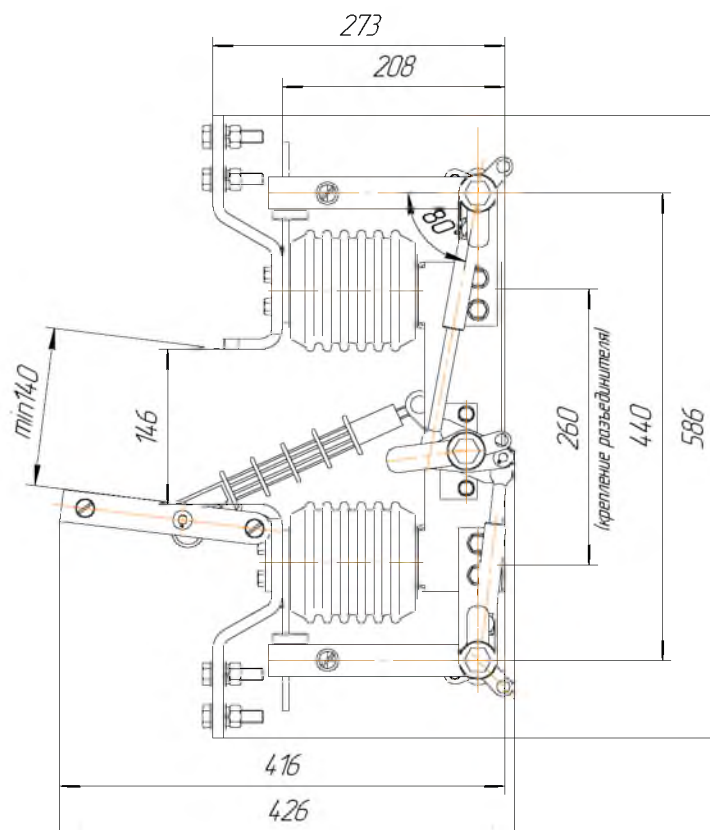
Разъединитель РВФп СЭЩ®-2-10/1600 У2 с главными ножами во включенном положении
